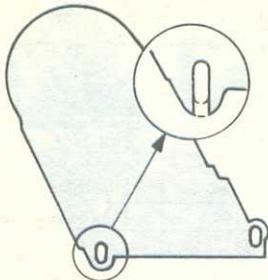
Доработка отверстия в защитной крышке двигателя ВАЗ-2105.
